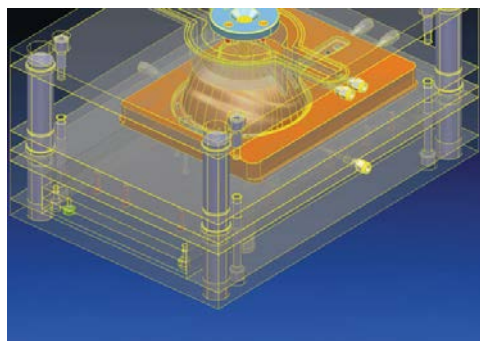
Готовая модель пресс-формы для изготовления дуршлага
